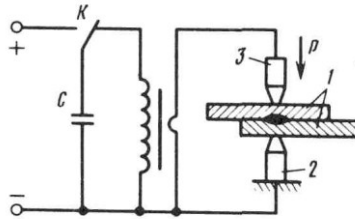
Установка для конденсаторной сварки: 1 — свариваемые заготовки; 2 — подвижный электрод; 3 — неподвижный электрод.
